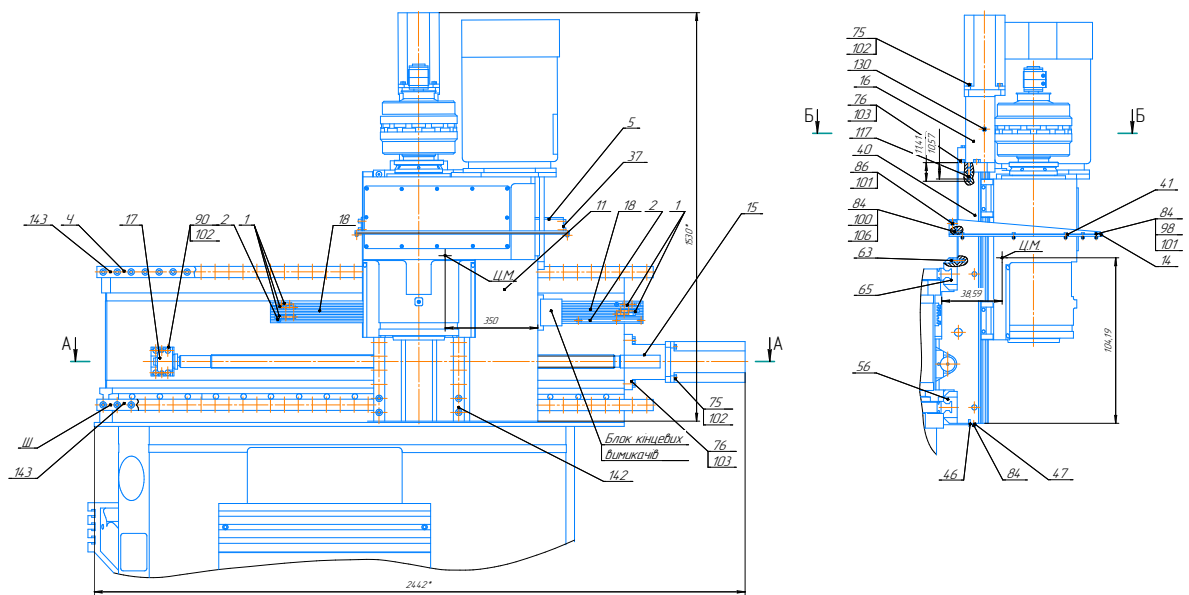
Загальний вигляд правого хрестового супорта верстата:
